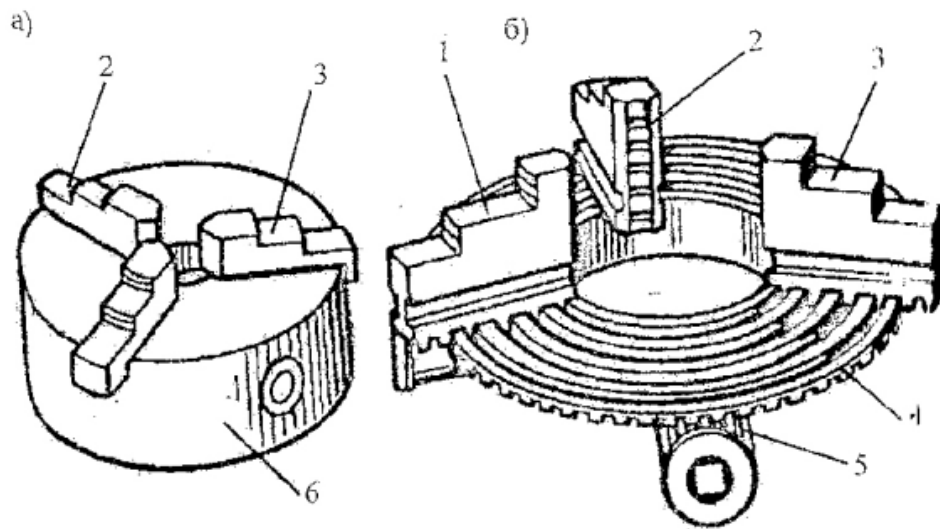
Самоцентрирующий трехкулачковый патрон: а – его общий вид; б – принципиальная схема привода кулачков; 1, 2 и 3 – кулачки; 4 – поворачивающийся диск; 5 – коническое зубчатое колесо; 6 – корпус патрона.
